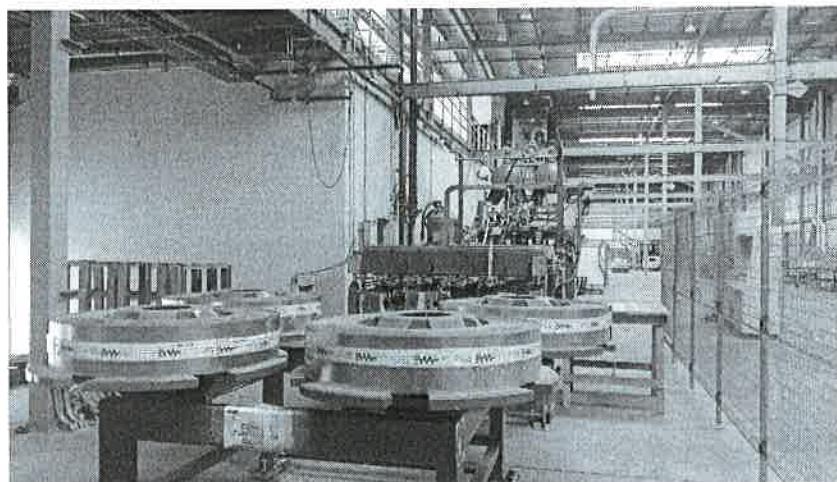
Vista de parte de la galera donde se ubica la rollería, grúa de elevación y máquina moldeadora.
